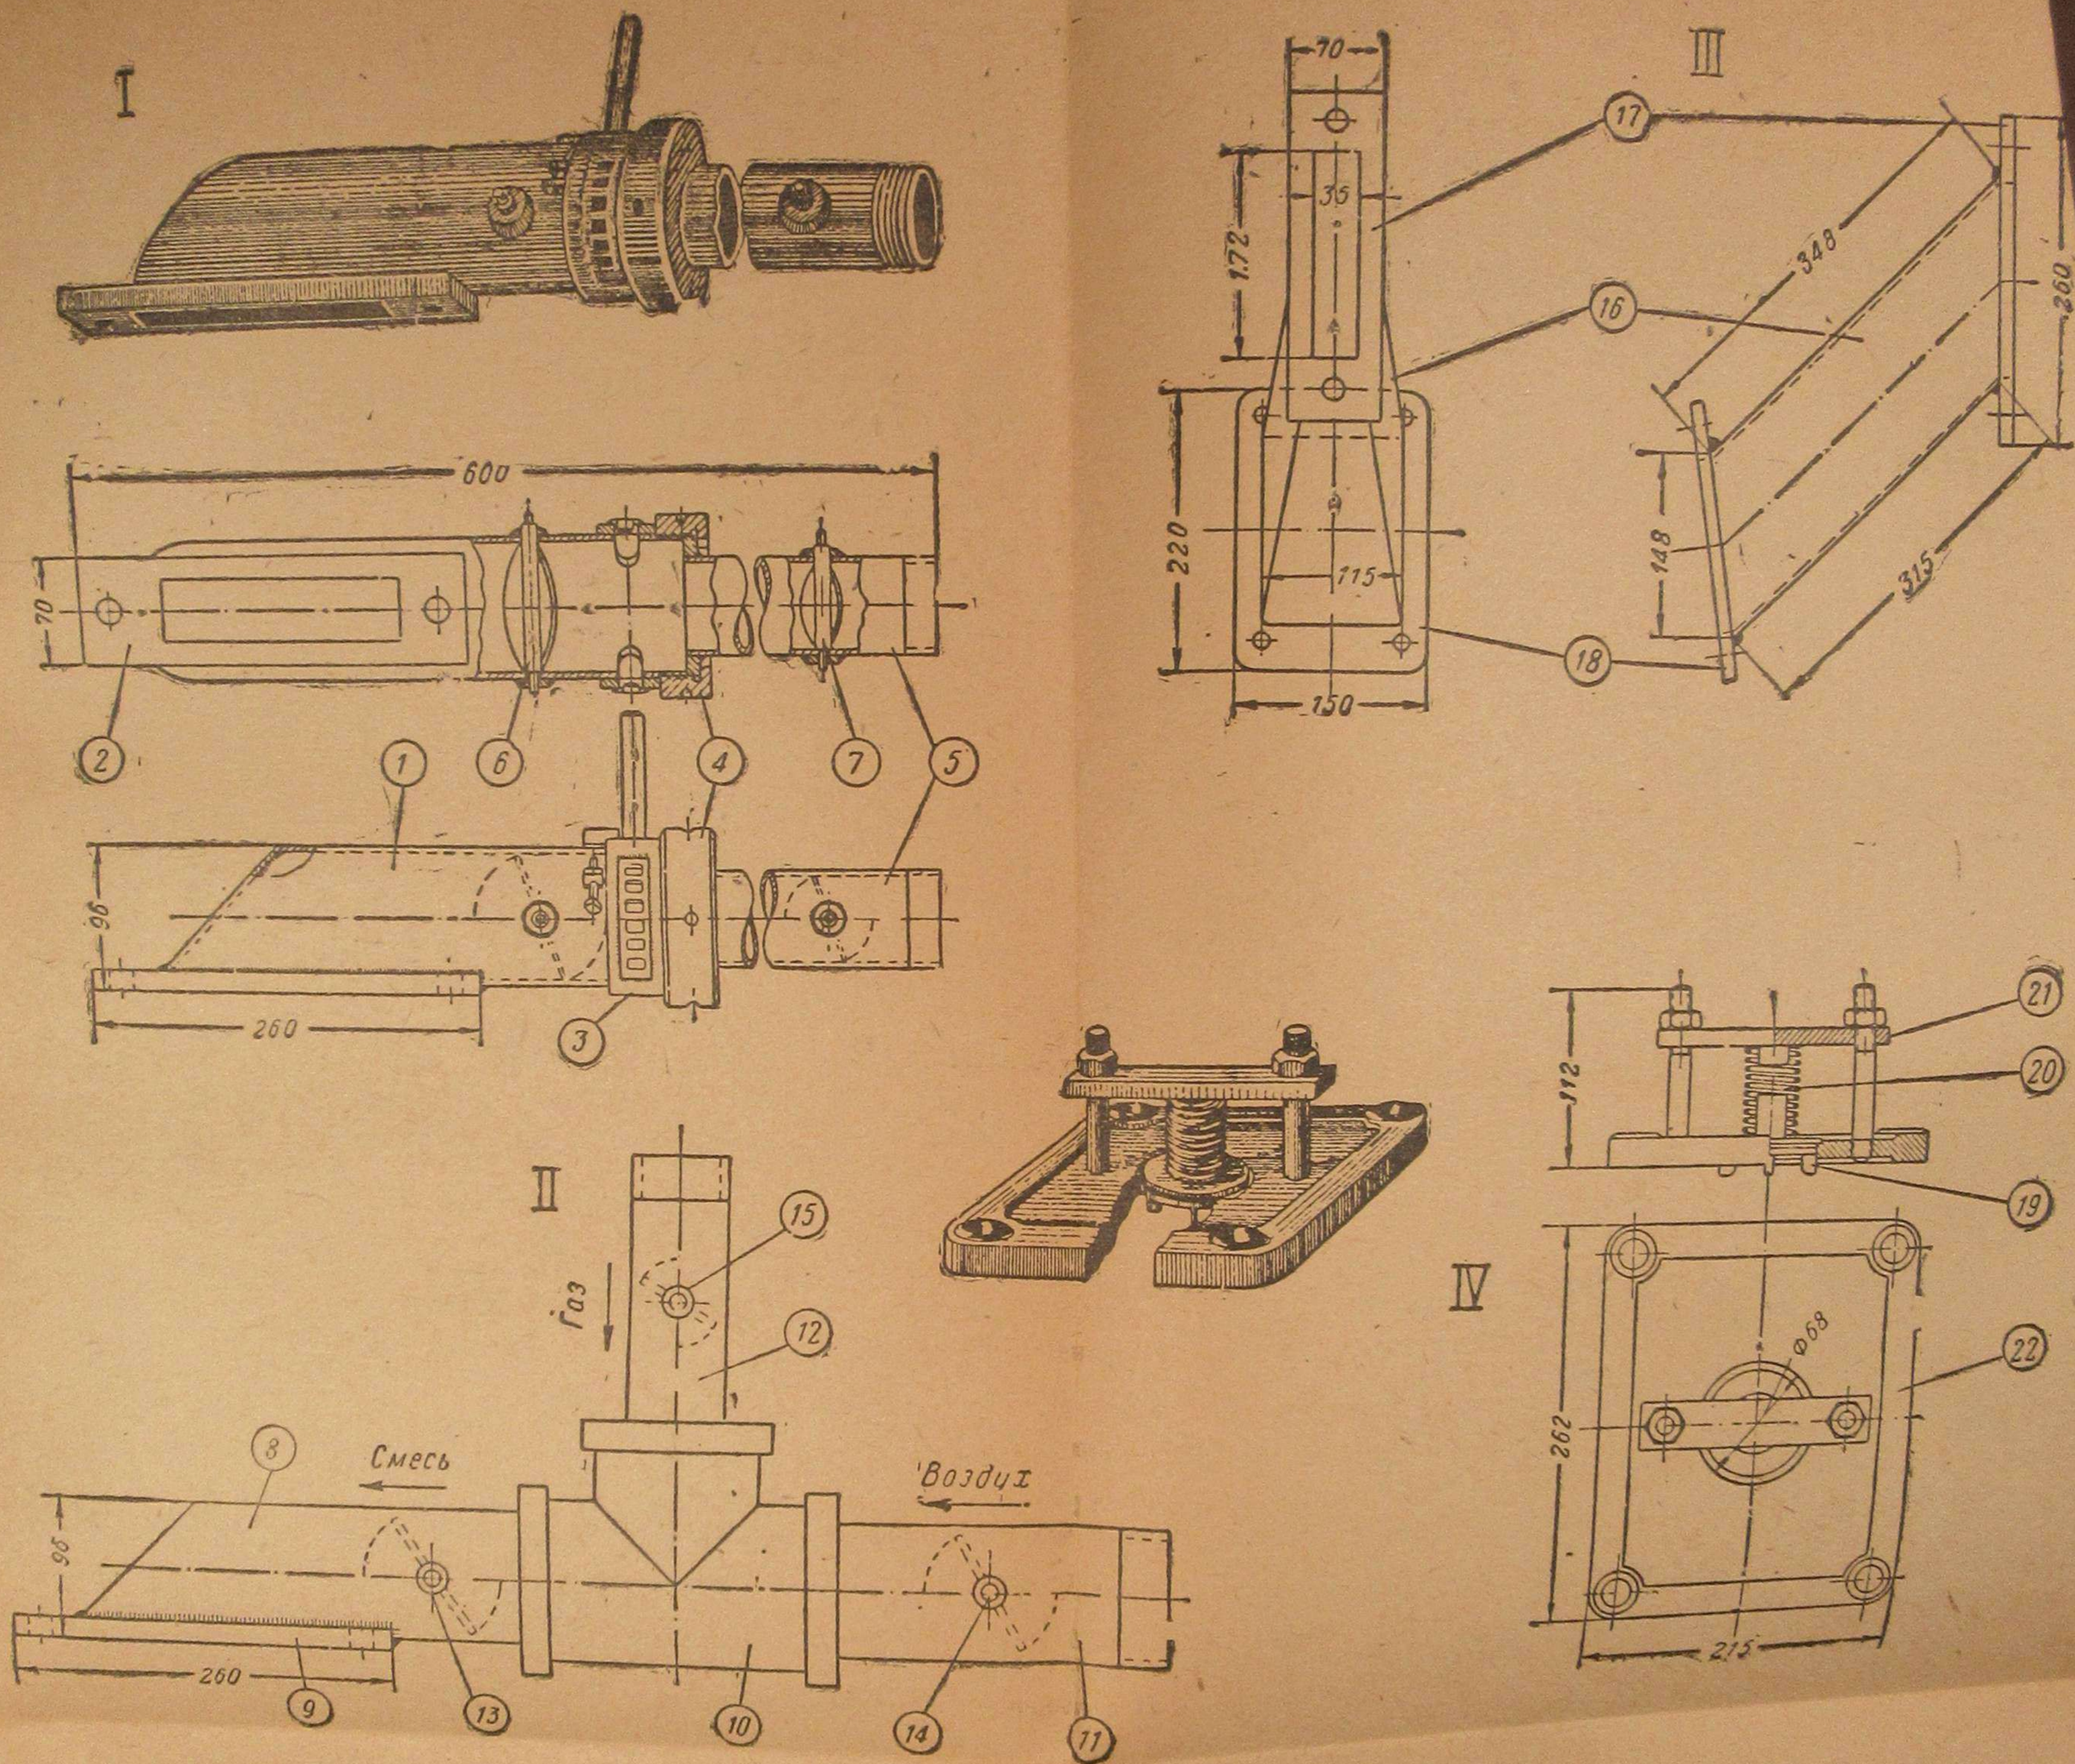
I. Смеситель с забором воздуха из помещения двигателя:
